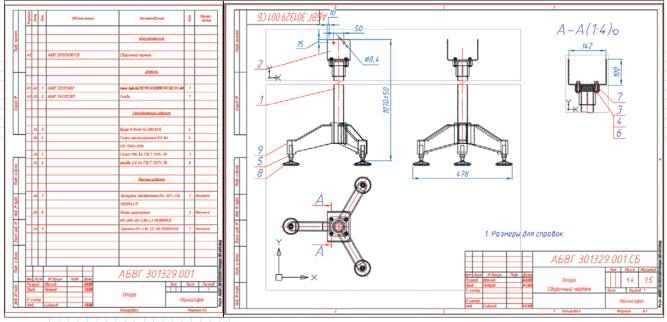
Сборочный чертеж опоры АБВГ.301329.001 со спецификацией
